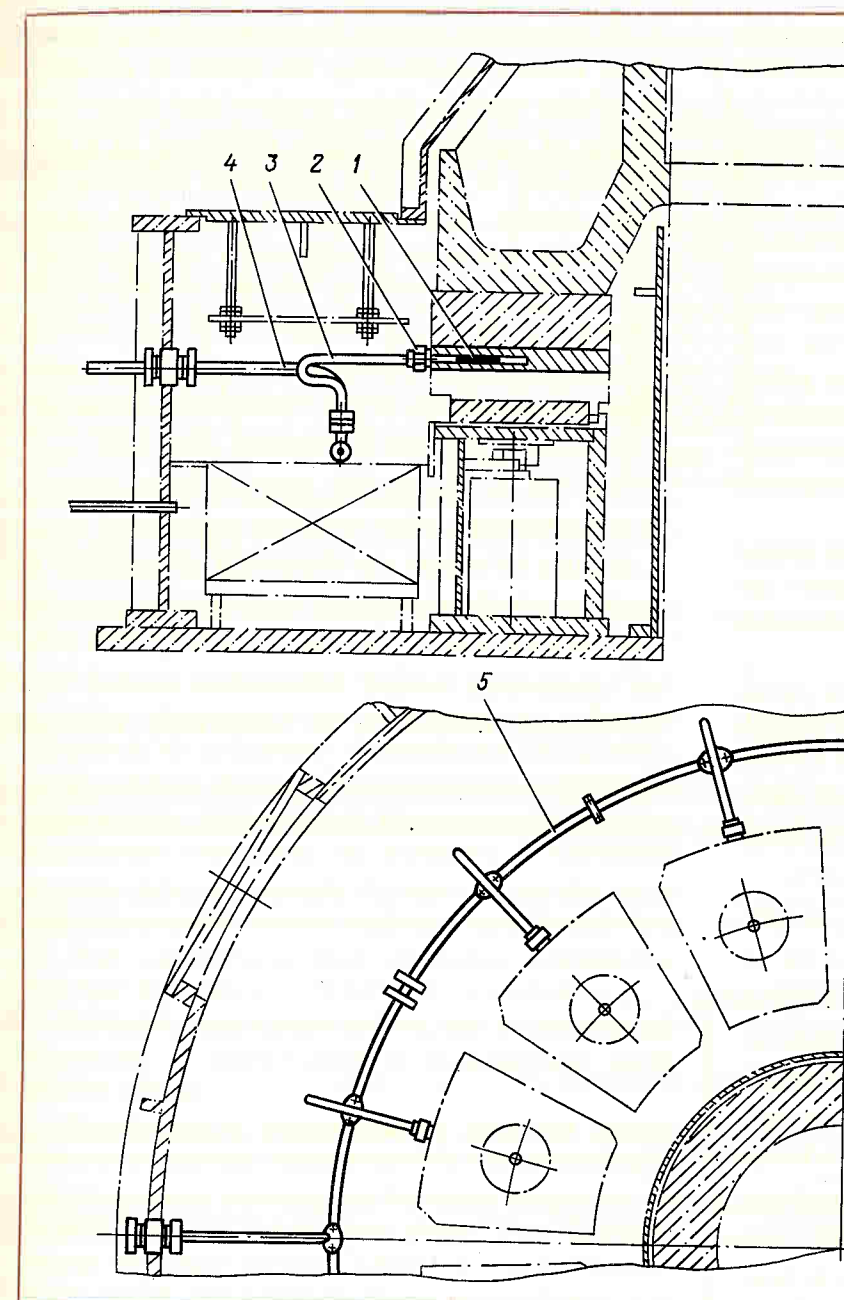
Общий вид устройства для принудительной подачи масла под давлением к трущимся поверхностям подпятника:
